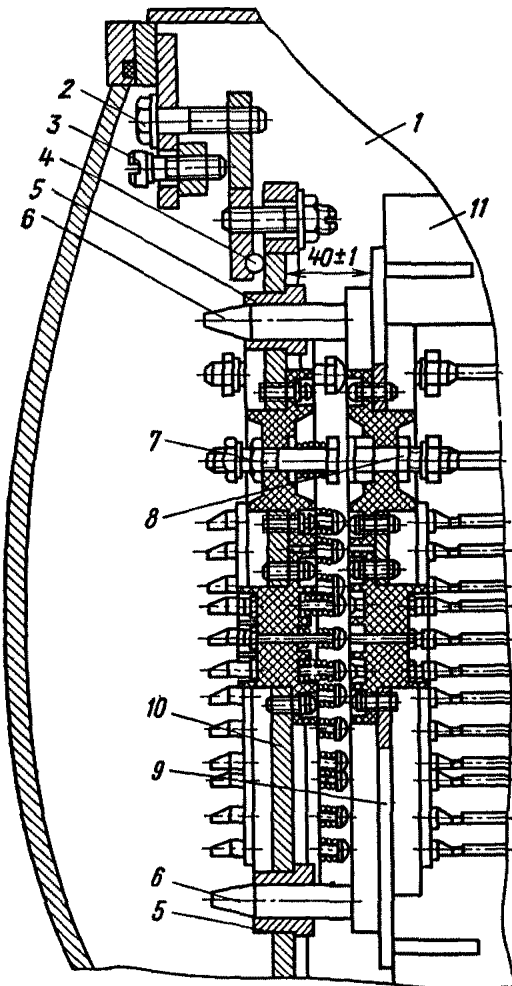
Стыковые контакты станций СУВ-1Л-100 и СУВ-2Л-120
